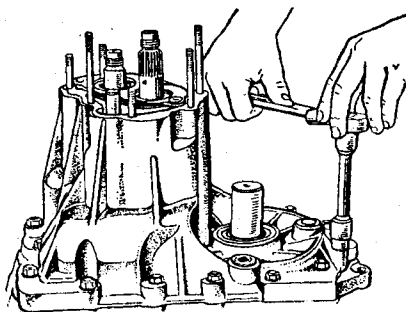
Отворачивание гаек шпилек крепления картера коробки передач
